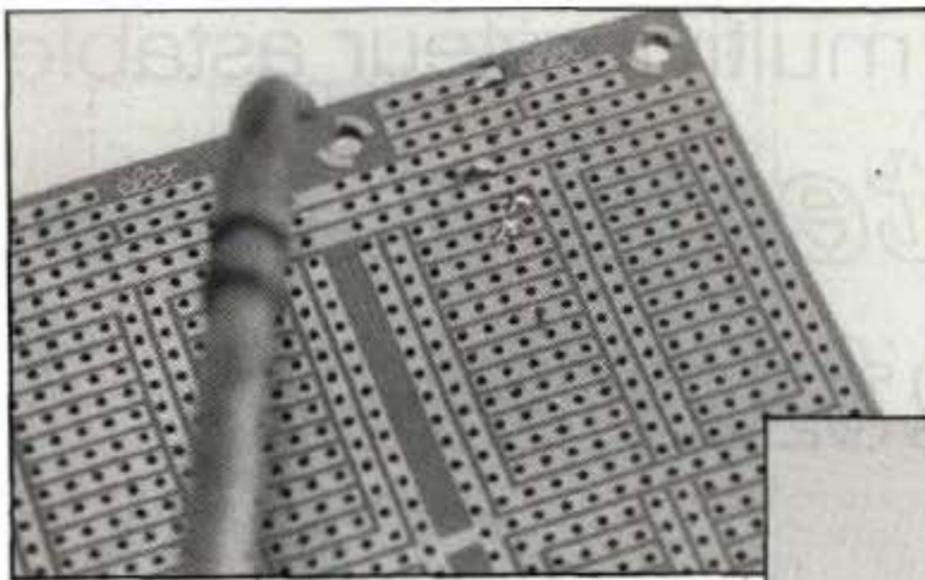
Laisser refroidir la soudure sans bouger.
